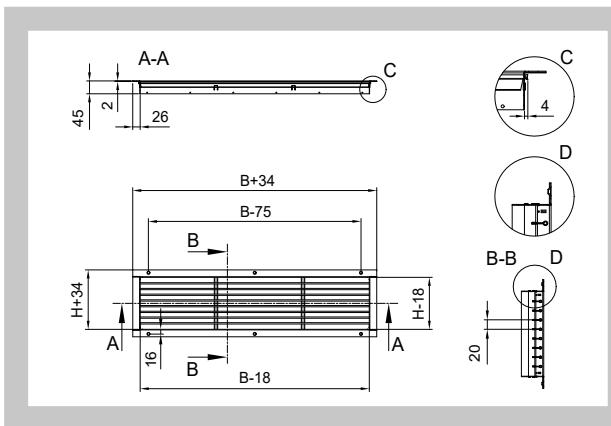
Einstellbare Lamellen horizontal - einreihig
